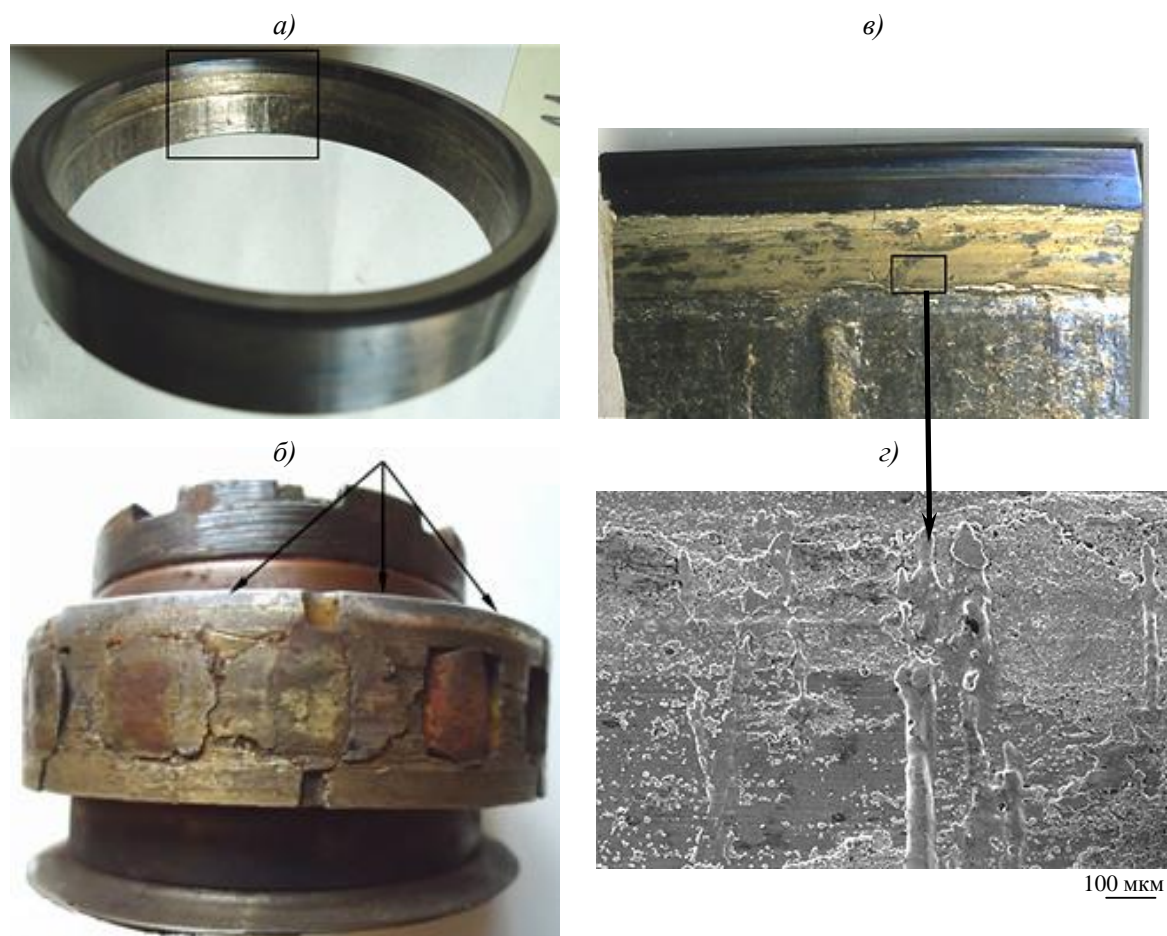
Внешний вид поврежденных деталей роликового подшипника:
